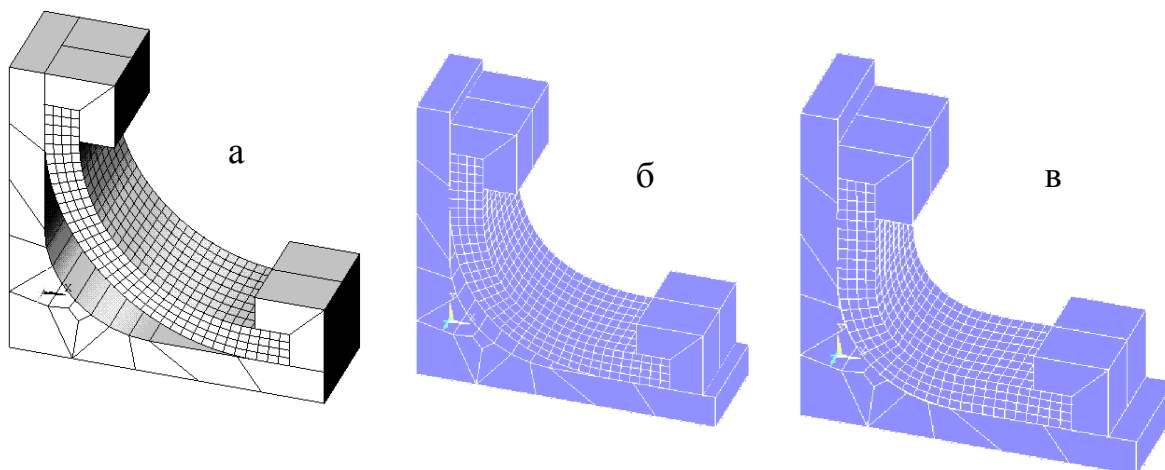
Ход процесса деформирования: а) – исходное положение; б) – положение заготовки перед контактом; в) – посадка наружного контура заготовки
